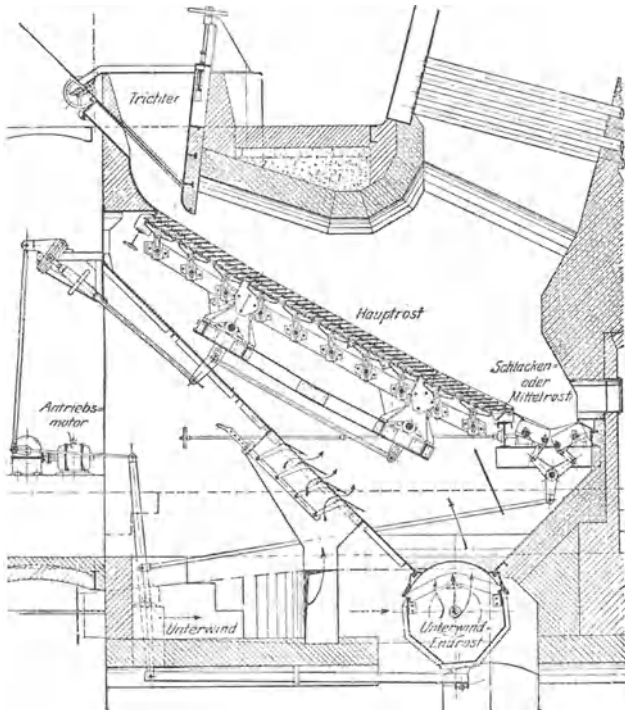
Evaporator-Schwingrost mit selbsttätiger Entschlackung.
